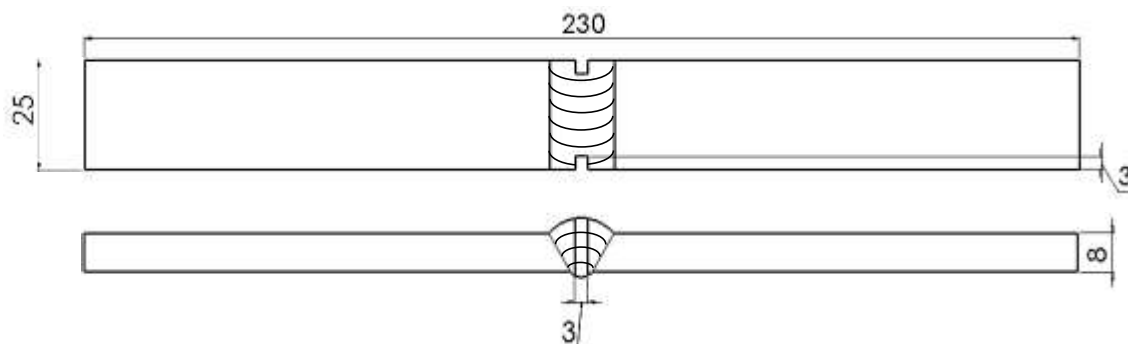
Dimensiones, probeta de ensayo nick break.
